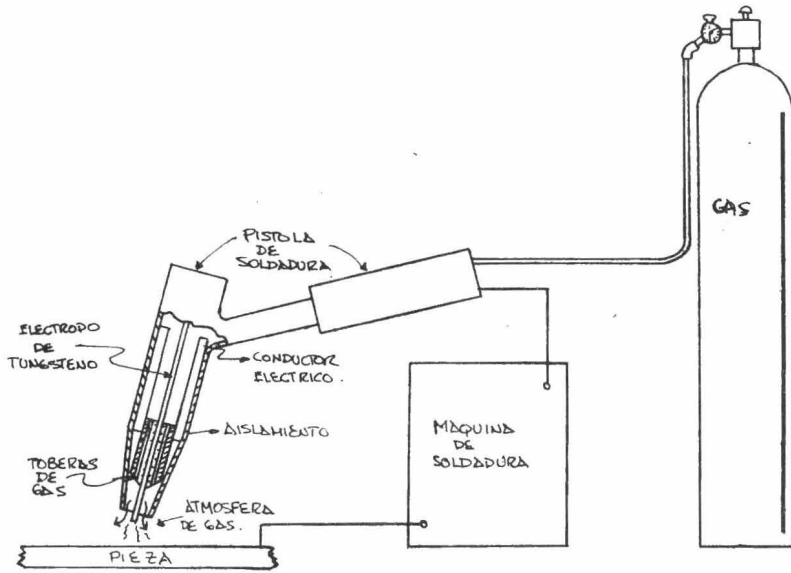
Procedimiento de Soldadura con Arco de Tungsteno - gas.
